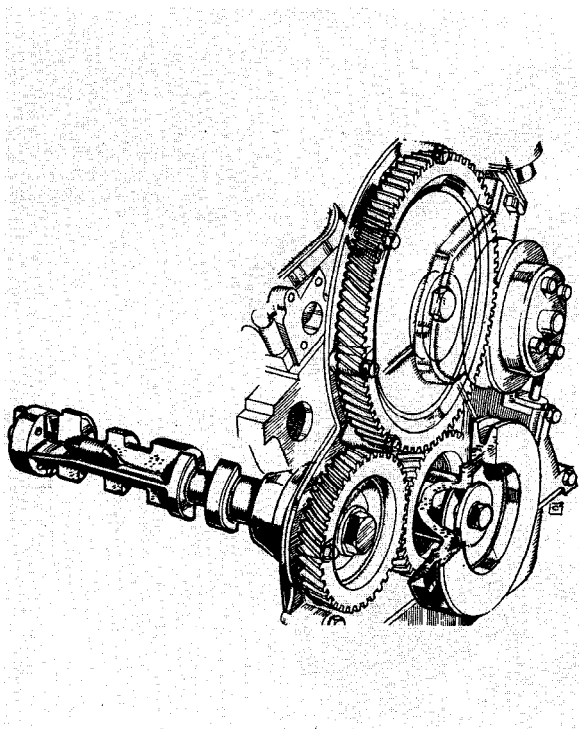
Eje equilibrador utilizado en un motor V-4 para contrarrestar el balanceo del motor (Ford de Inglaterra).
